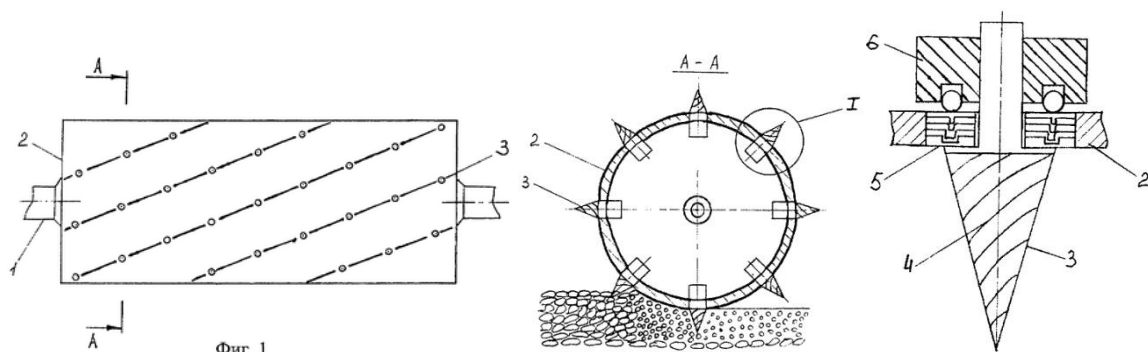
Схема почвообрабатывающего орудия с вибрирующим обгонным устройством
